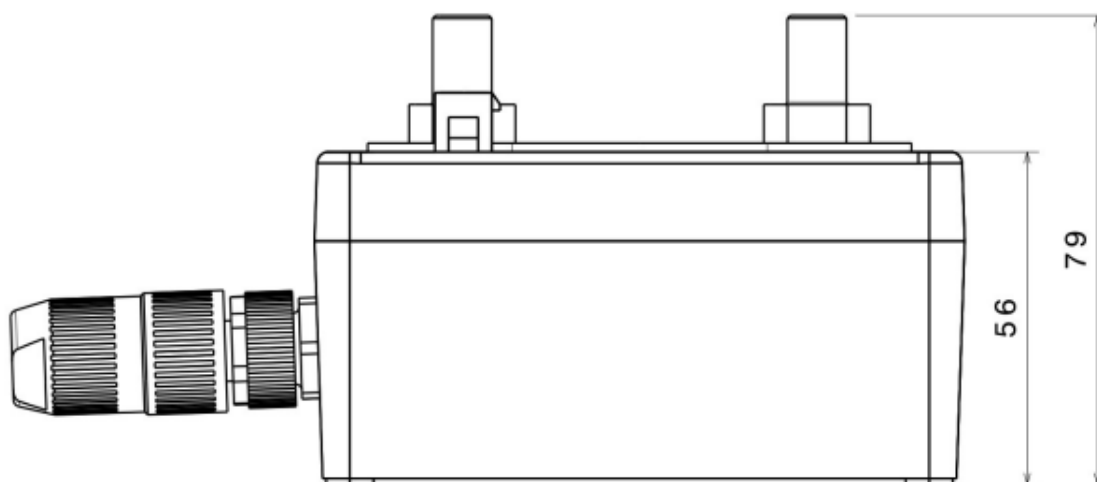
Vista da face lateral (dimensões em mm). Fonte: Formula Student Germany.
